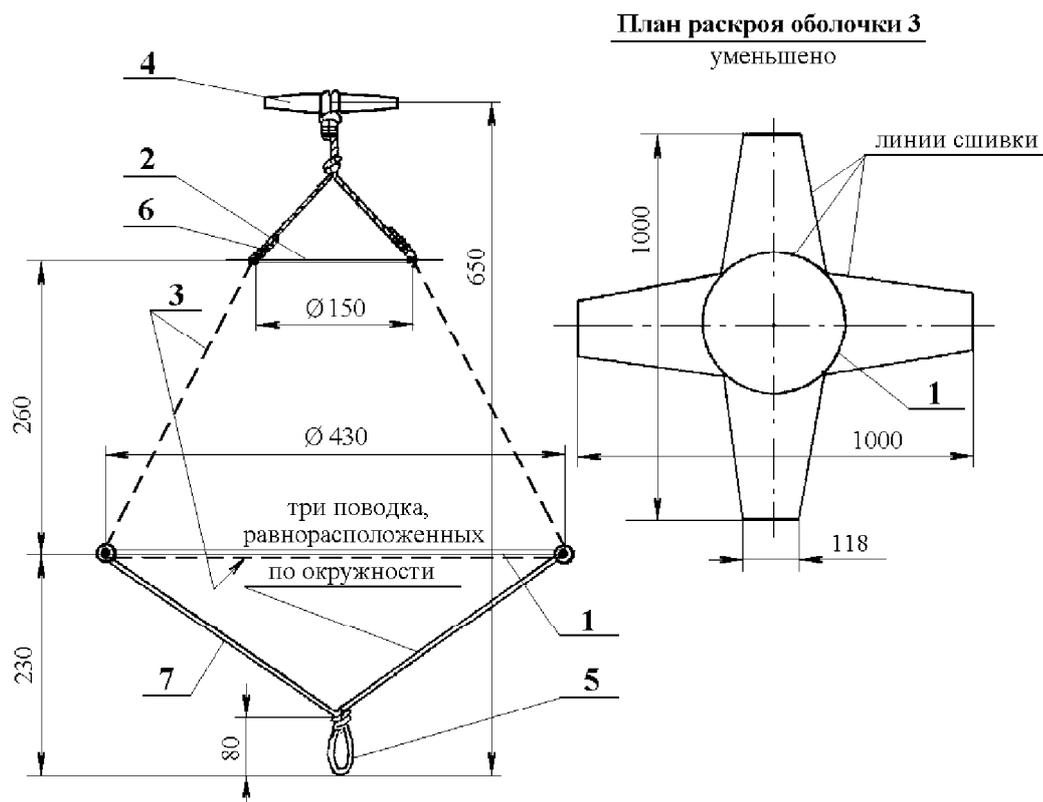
Садок для подращивания устриц: 1 – обруч; 2 – обруч малый; 3 – оболочка сетная; 4 – штырь; 5 – петля; 6 – поводок верхний; 7 – поводок нижний
